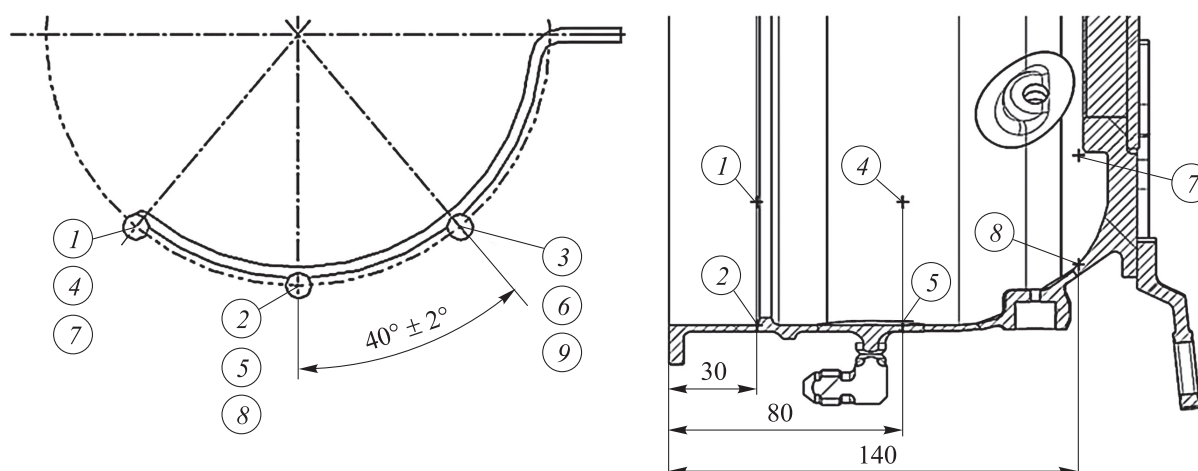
Схема расположения термопар на корпусе КС испытания на стенде
